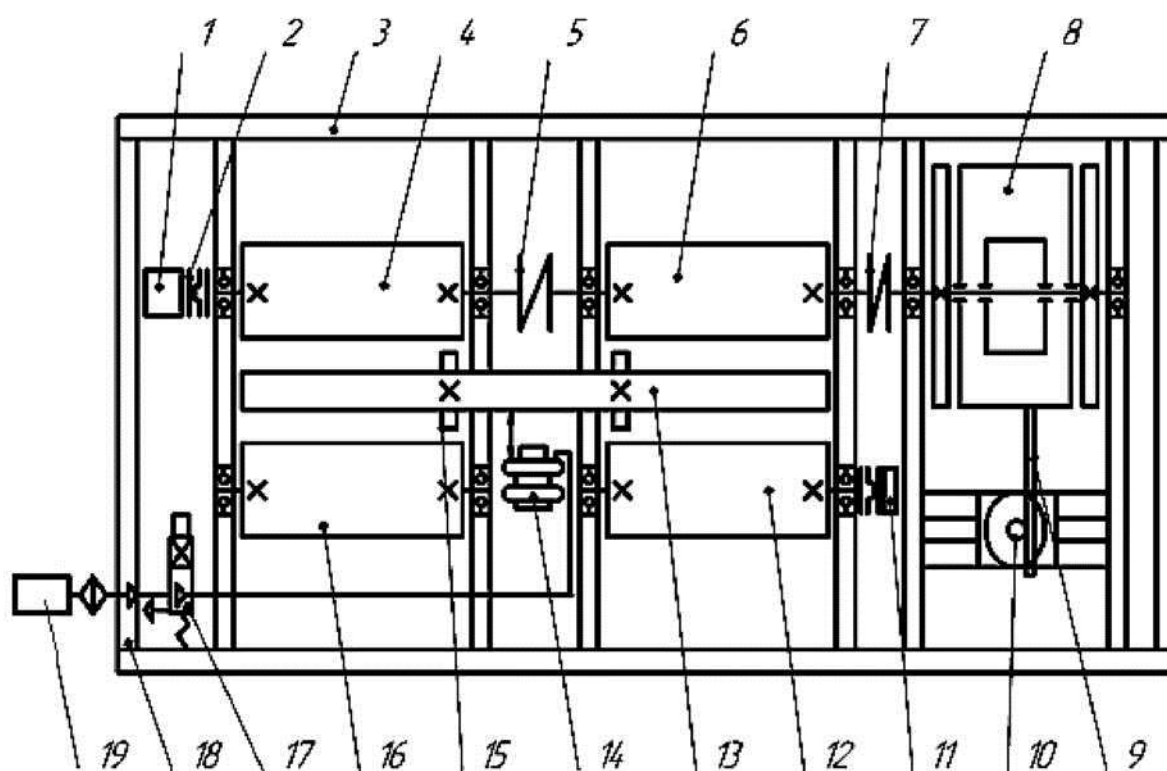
Пневмокинематическая схема опорного устройства:
